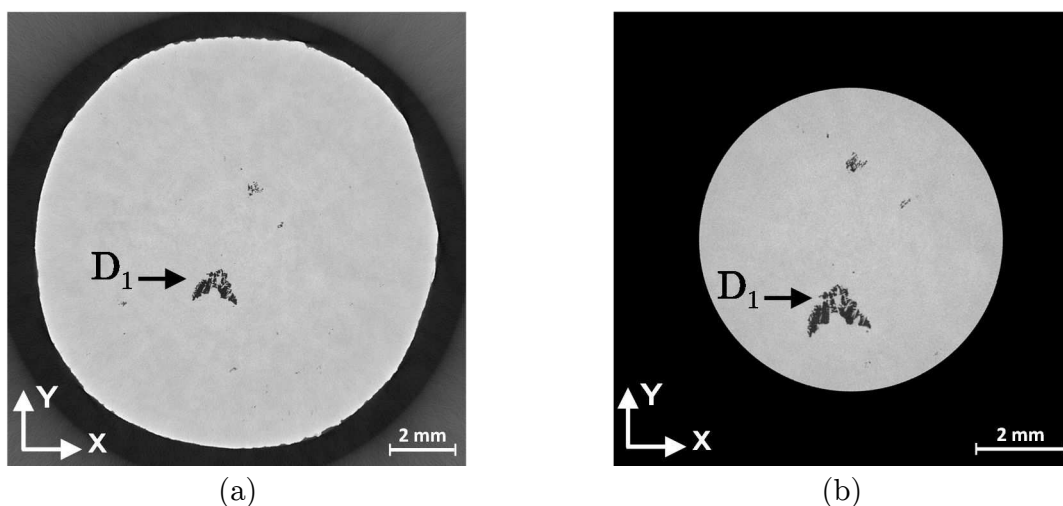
(a) Image tomographique prise dans la section utile du brut de coulée de l'éprouvette 28-2 (RC 1) avant usinage, taille du voxel =  $8 \mu\text{m}$ , (b) définition d'un diamètre de la zone utile de l'éprouvette de 6.93 mm
